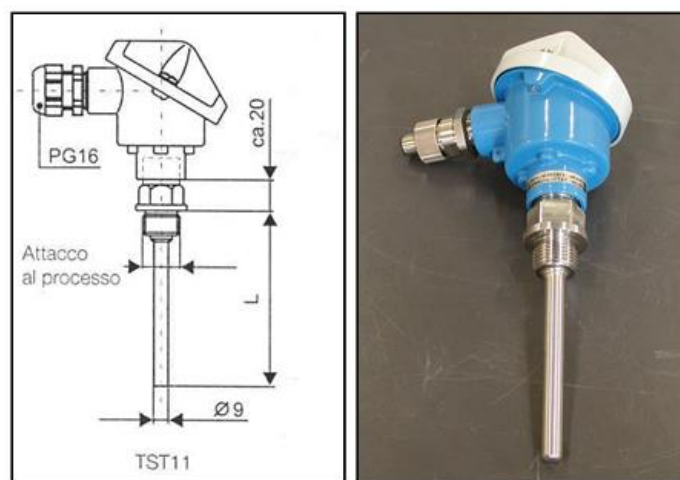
Disegno e foto TST11 (Fonte: Endress+Hauser)
